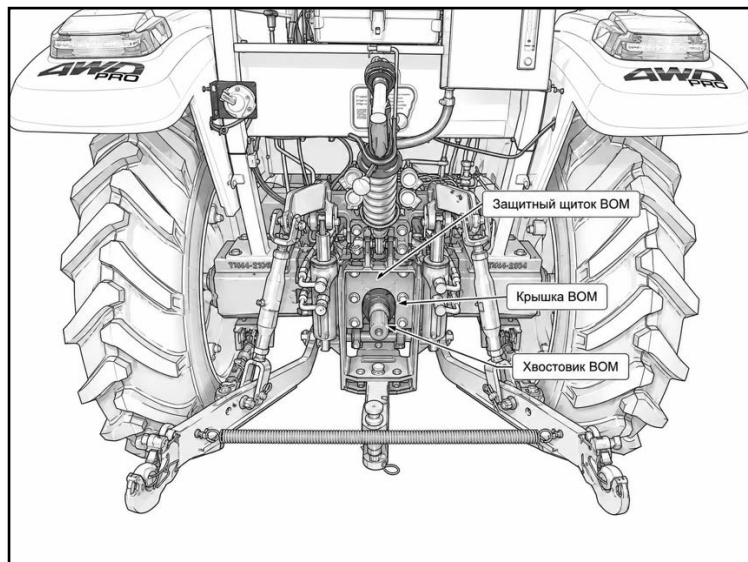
Защитный щиток и крышка вала отбора мощности
